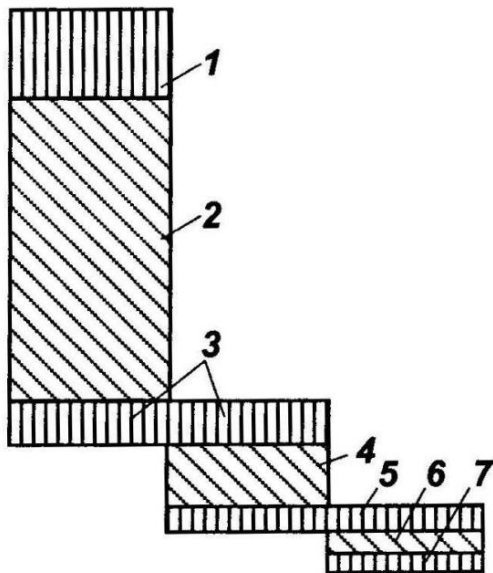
Схема розташування припусків і допусків при обробці вала: 1 – допуск на виготовлення заготовки; 2 – припуск на попередню обробку; 3 – допуск на попередню обробку; 4 – припуск на шліфування; 5 – допуск на шліфування; 6 – припуск на доведення; 7 – допуск на доведення
